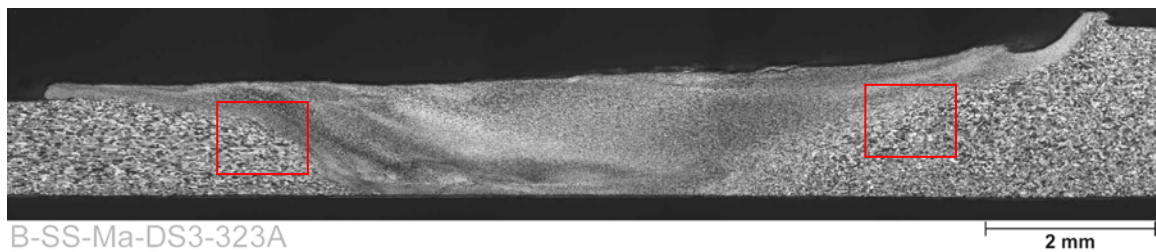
Macrografia de uma junta 6181 T4 soldada com 10 m/min. Ataque químico: Barker.
